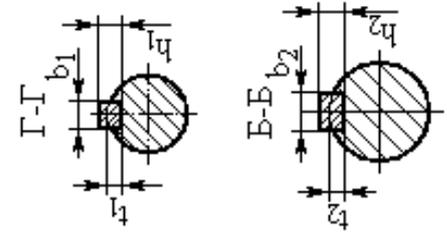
Цилиндрический трехступенчатый редуктор типа ЦЗУ
